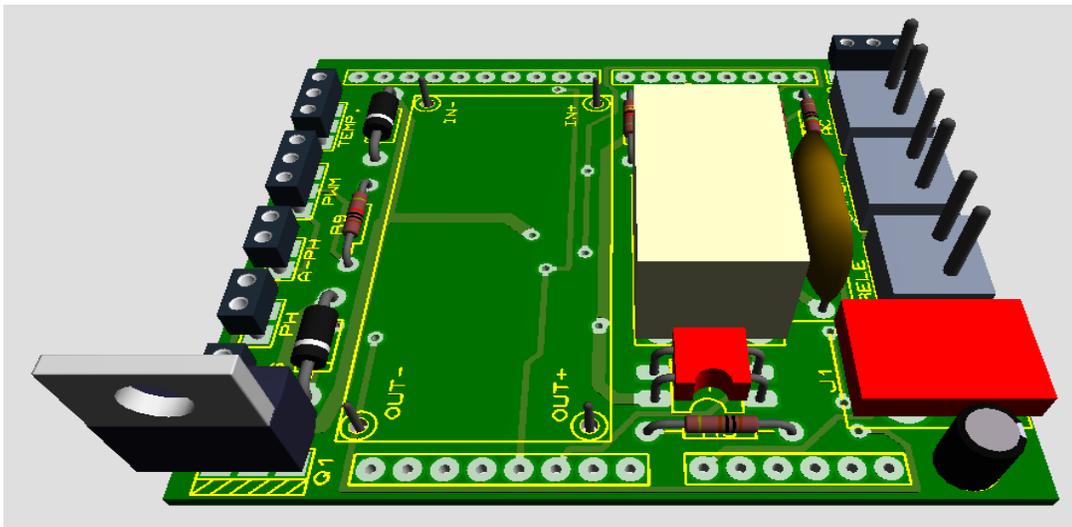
Tarjeta diseñada a dos capas para impresión en PCB vista lateral. Fuente el autor.
